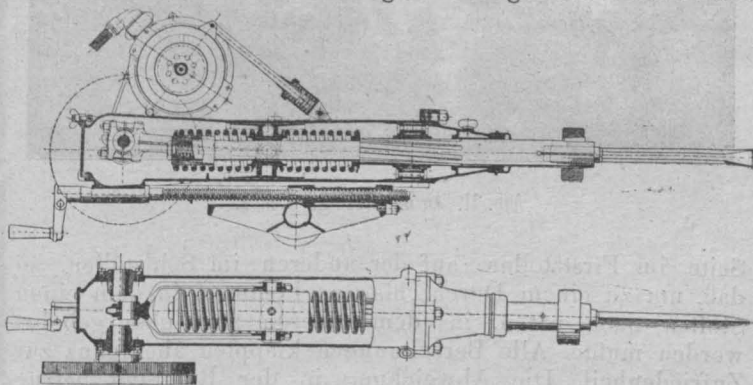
Elektrische Kurbelstoßbohrmaschine.
